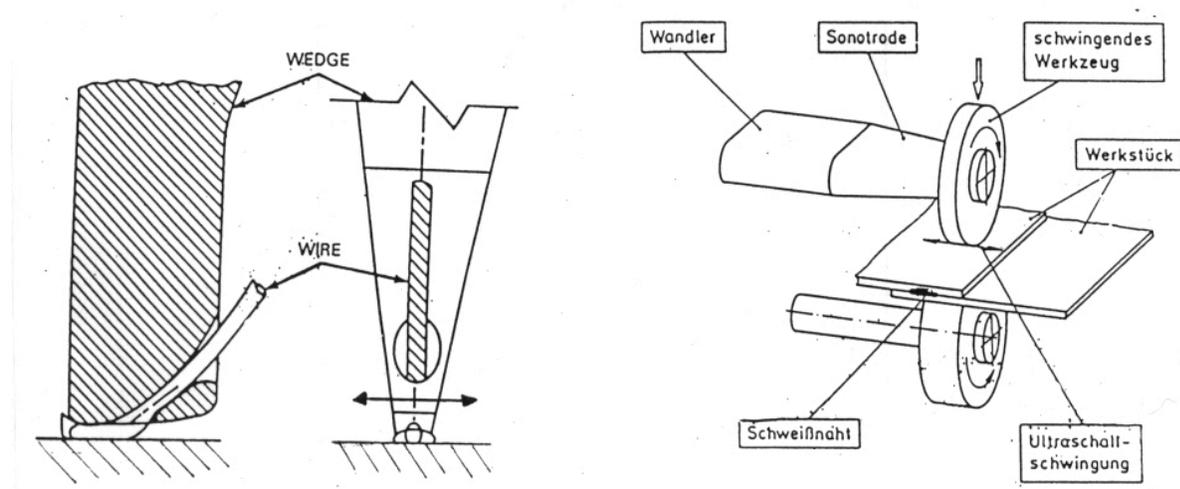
Plusieurs dispositions de soudage par ultrason. a) soudage par point dans des connecteurs électroniques et b) arrangement pour le soudage par ligne de deux papiers métalliques avec une sonotrode révoltante.
